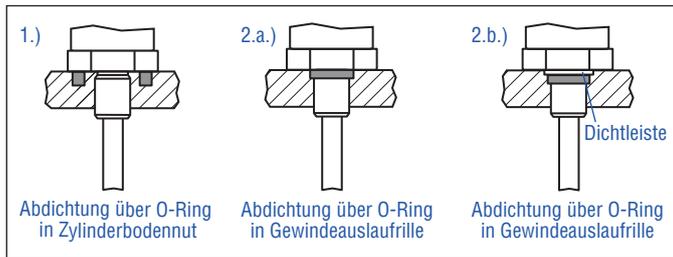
Möglichkeiten der Abdichtung für Standard Gewindeflansche (GH5-M/S) 1. + 2.a. und für Gewindeflansche mit Dichtleiste (GH5-T) 2.b.
